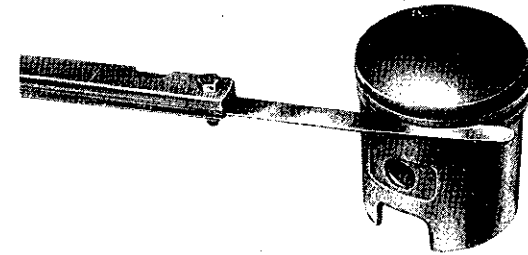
Messen des Höhspiels der Kolbenringe mittels Fühllehre
